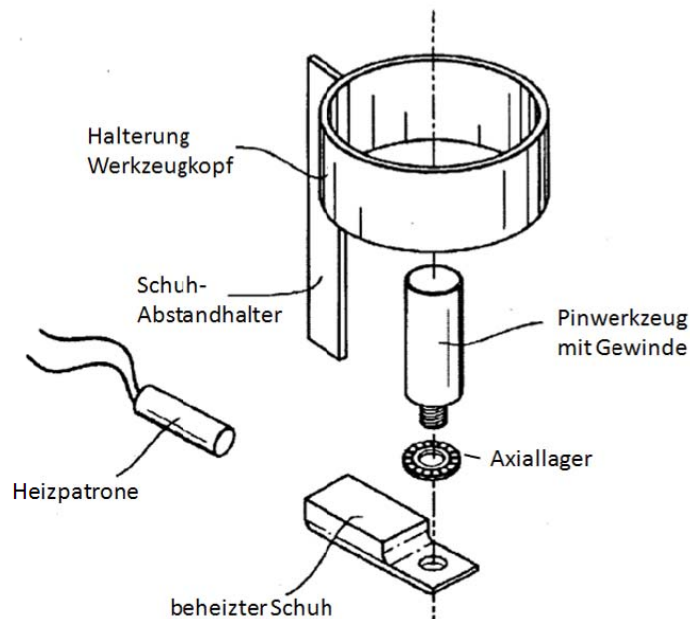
Hot-Shoe-Tool: Prinzipieller Aufbau [1 S. Fig.5]
